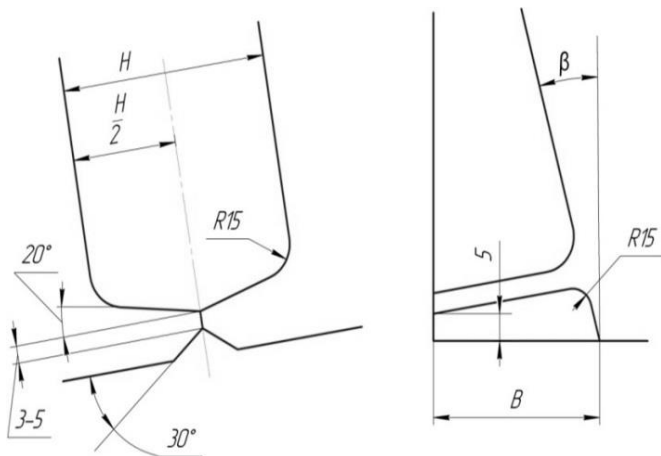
Протяжной ручей открытого типа, расположенный под углом у оси штампа
